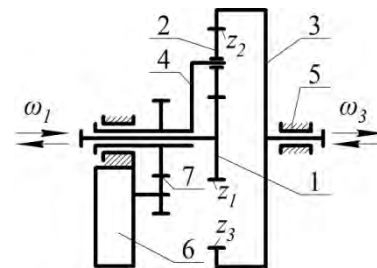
Схема пристрою для керування змінами швидкості через водило: 1 – сонячне зубчасте колесо; 2 – сателіти; 3 – епіцикл; 4 – водило; 5 – корпус
